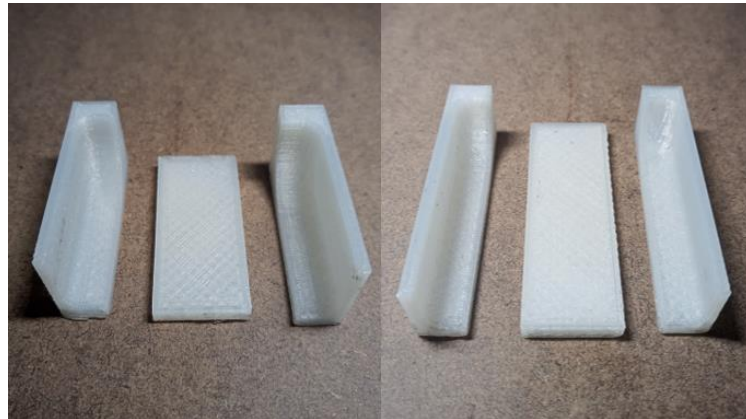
Molde impreso en 3D del sensor de fuerza resistivo.
